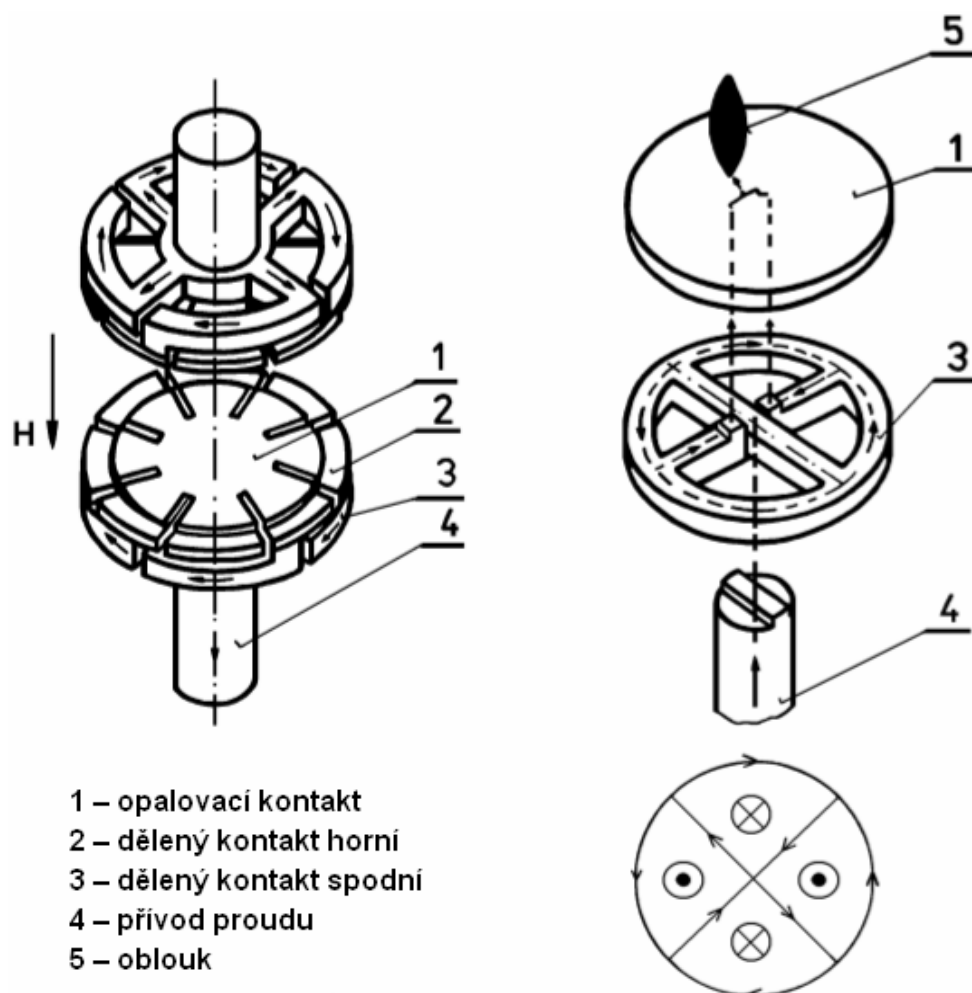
a 11.10. – Konstrukce axiálních vakuových zhášedel
